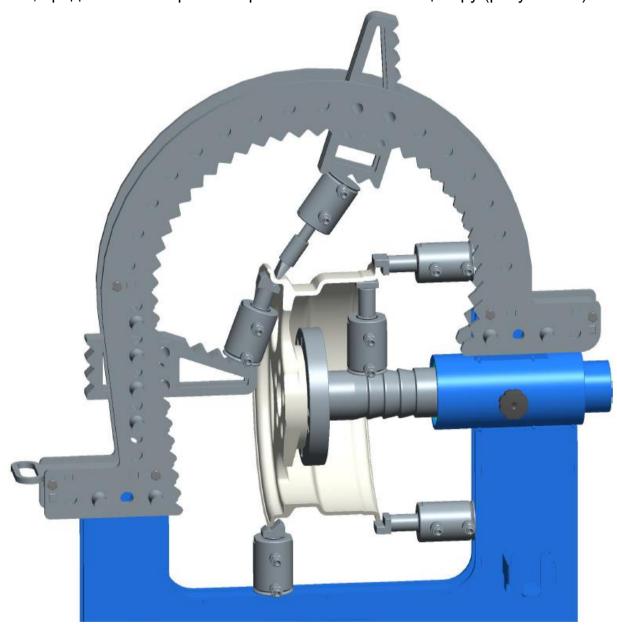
Примеры расположения гидроцилиндра с различными типами насадок при правке диска
